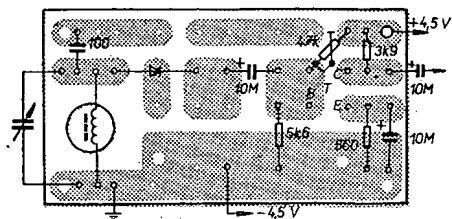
Rozmístění součástek pro krytálku se zesilovačem podle obr. 5c, AR 5/71
